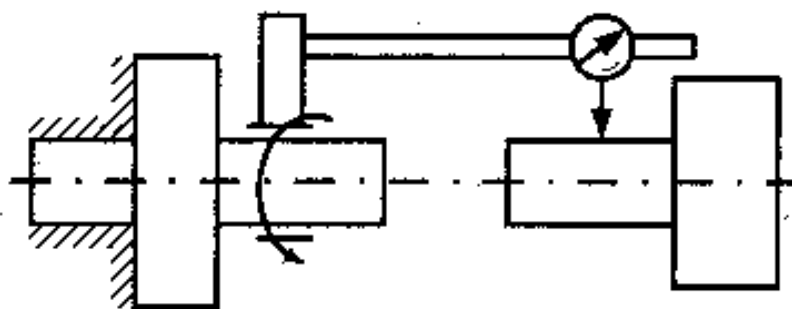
Схема контроля соосности цилиндрических поверхностей
